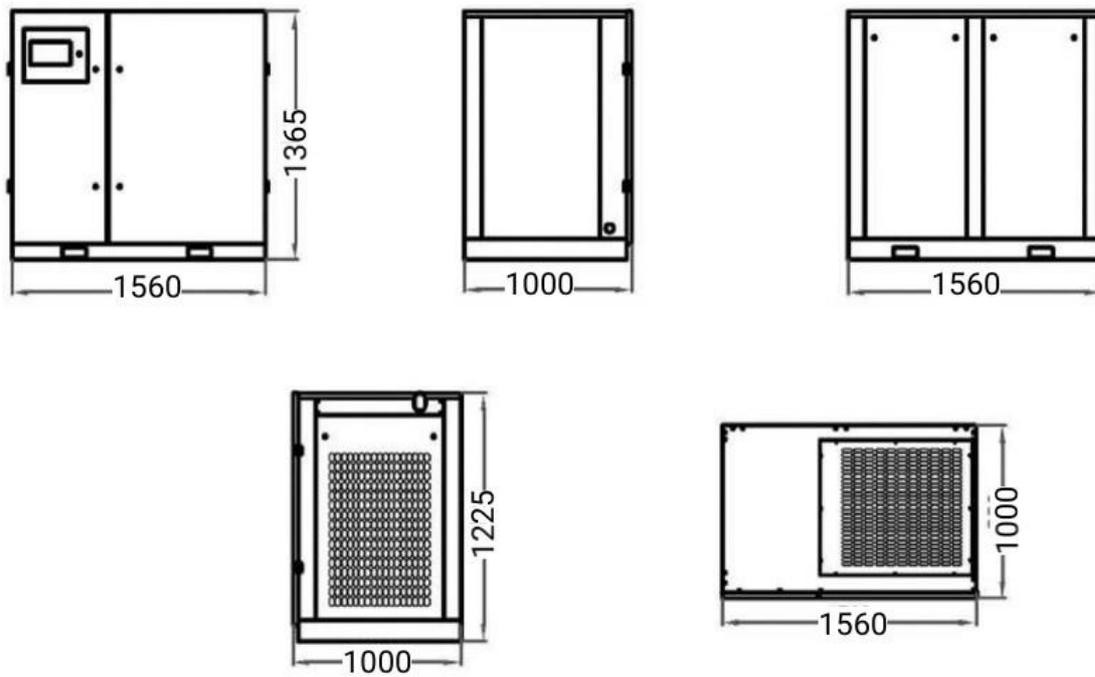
Габаритные размеры компрессоров BRM-37-45A
